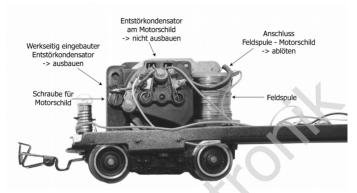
Scheibenkollektor-Motor mit Feldspule (vor dem Umbau). Die werksseitig eingebaute Entstördrossel ist nicht sichtbar, sie muss ausgebaut werden.
